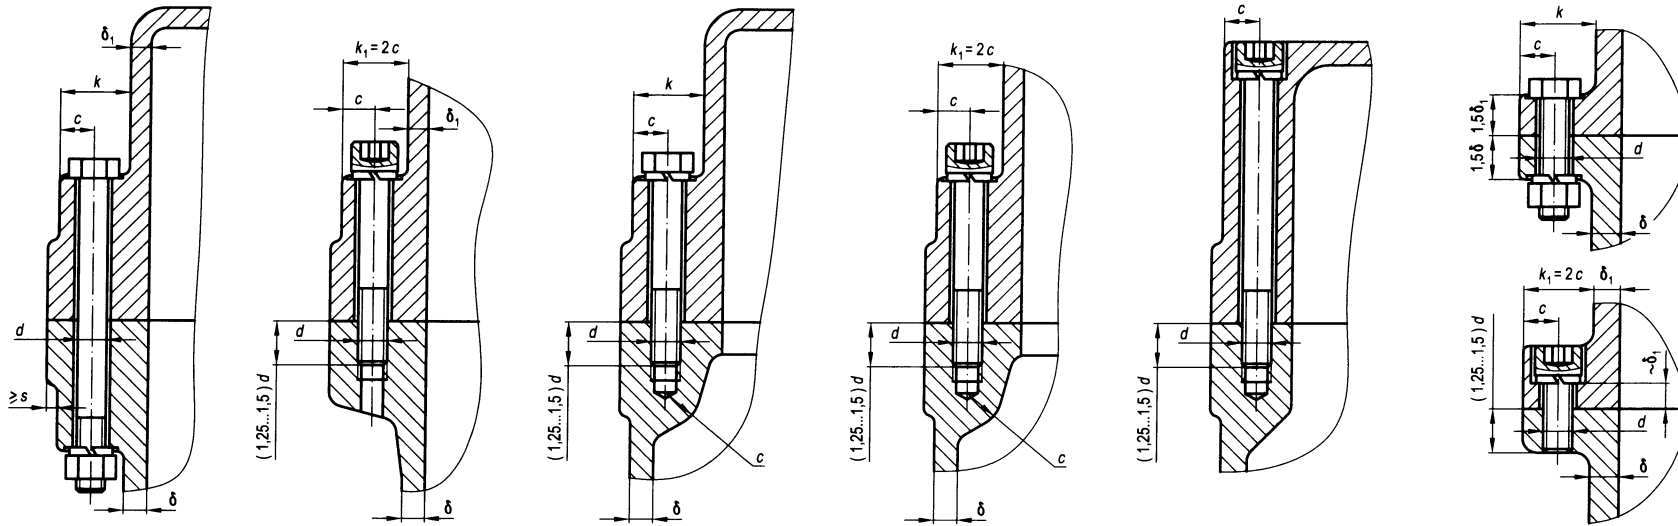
Приливы под болты на продольных фланцах корпуса (размеры см. в табл. 23.2.1)
